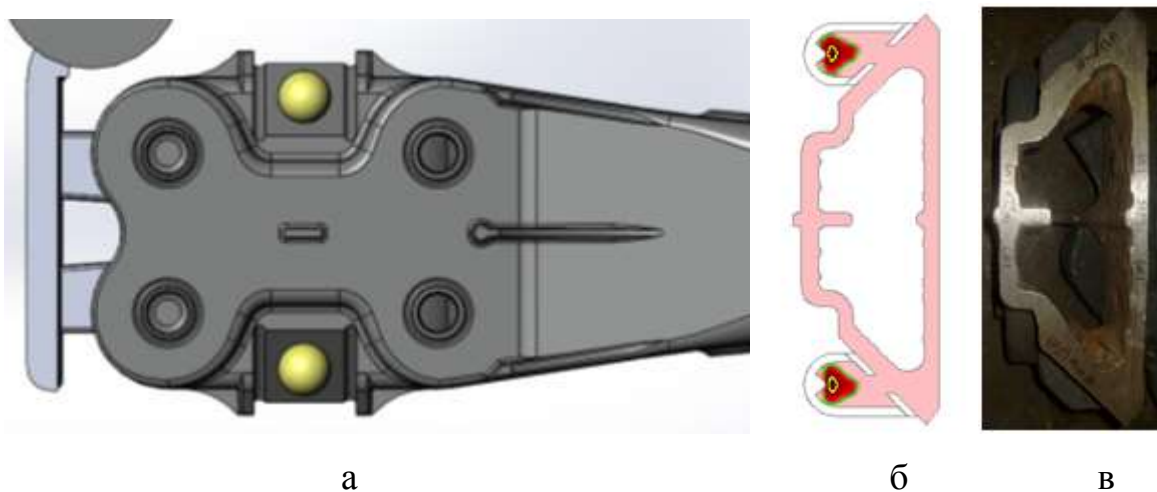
Геометрическая модель (а) отливки «Балка надрессорная» с установленными прибылями; прогнозируемое (б) и фактическое (в) отсутствие усадочных дефектов в тонких стенках отливки
